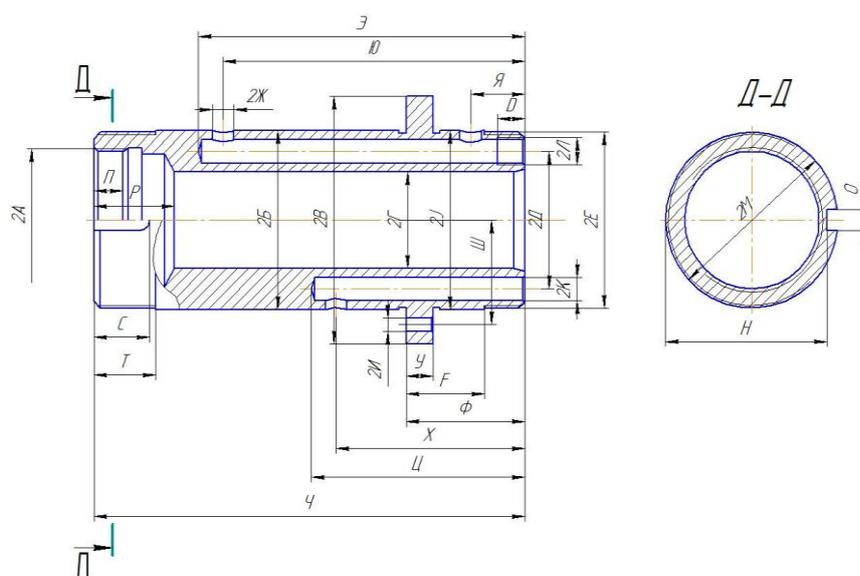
Кодировка размеров детали "Обойма штока"
